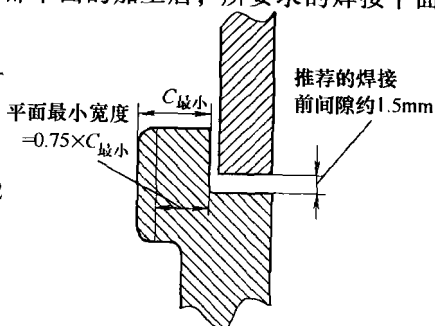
要求的焊接间隙和最小平面宽度
